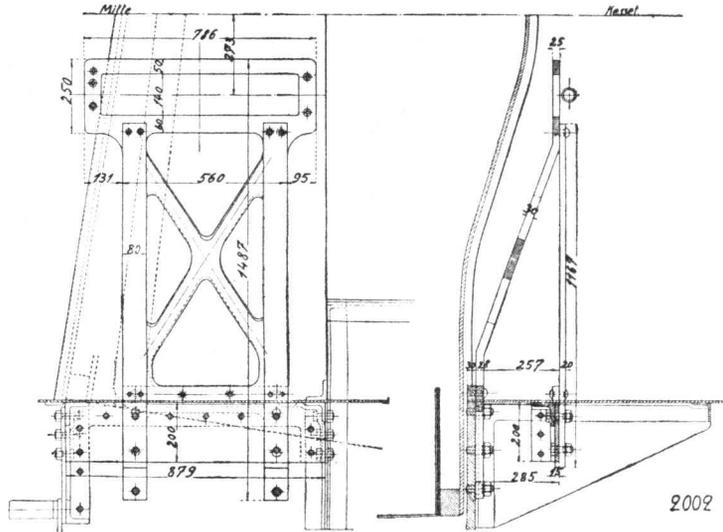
Befestigung des Steuerbocks (Reversierständer). (Neuere Ausführung.)
